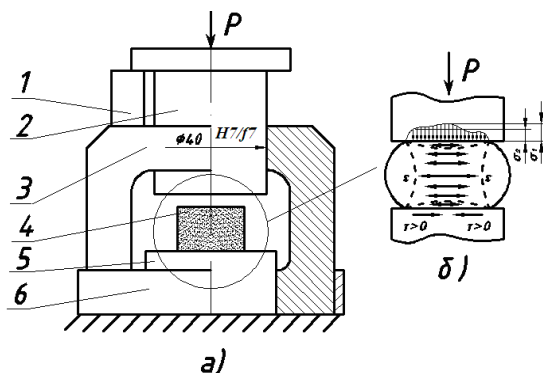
Приспособление для осадки образцов (а) и схема действия напряжений и деформации при свободной осадке цилиндрических образцов
